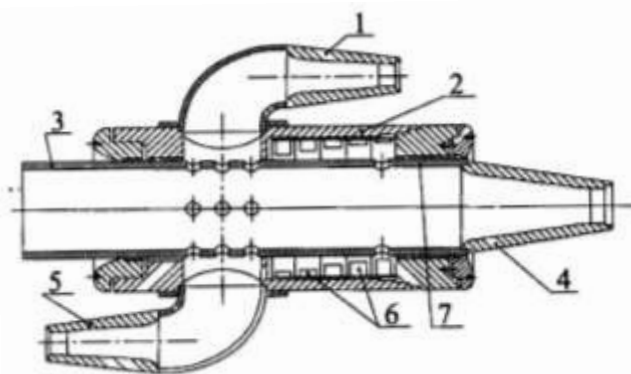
Гідромоніторна головка: 1 – відбійна насадка; 2 – корпус, що обертається; 3 – ствол; 4 – врубова насадка; 5 – транспортуюча насадка; 6 – гальмо; 7 – підшипник
